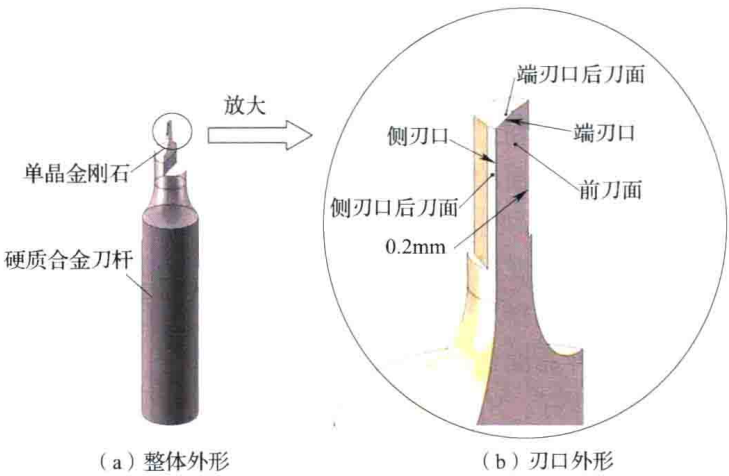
焊接刀杆式单晶金刚石微型圆柱立铣刀
